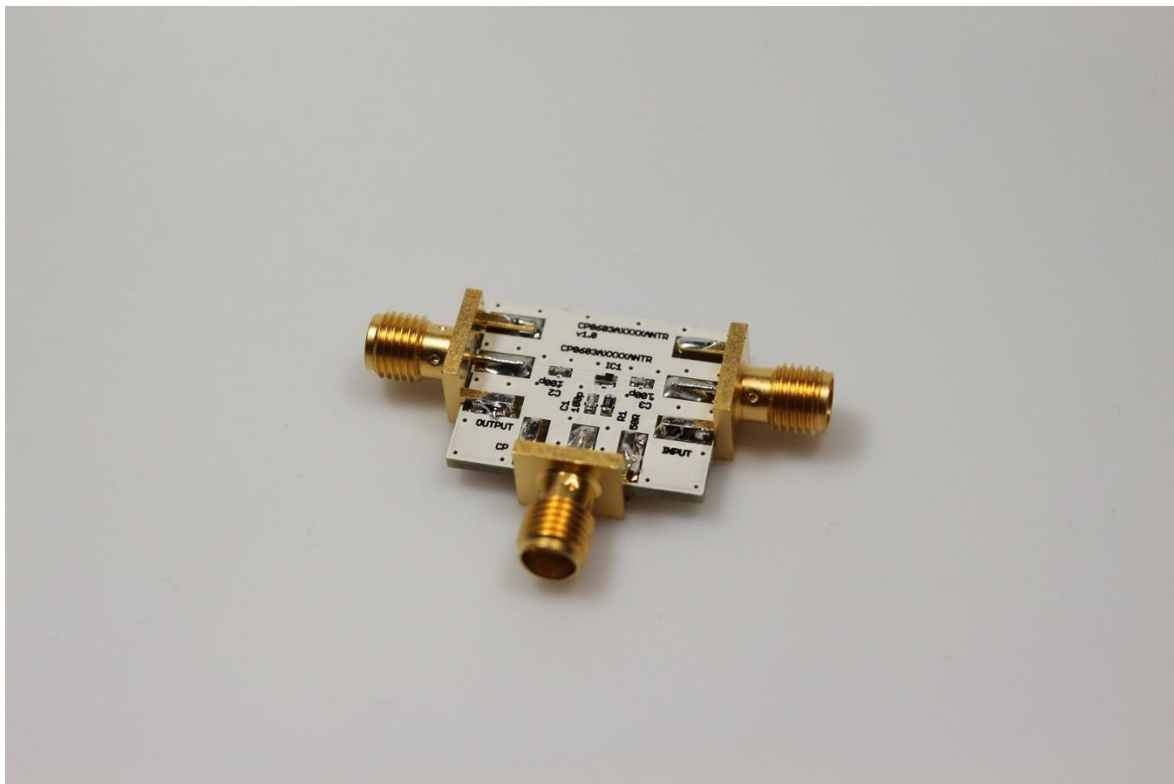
Hotový tištěný spoj pro součástku VMMK-2503
